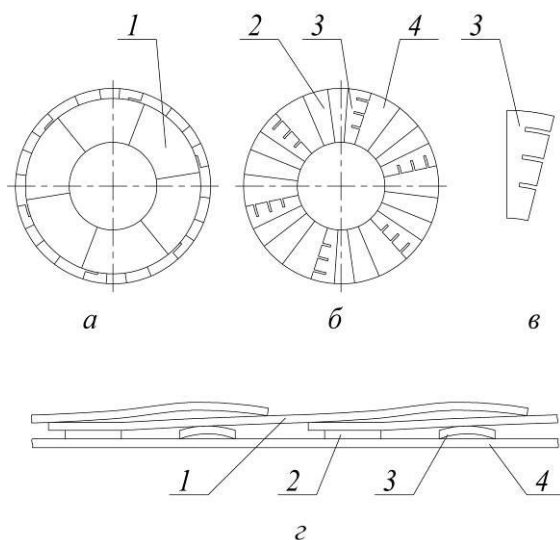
Лепестковый газодинамический подшипник осевой TFGB44.
